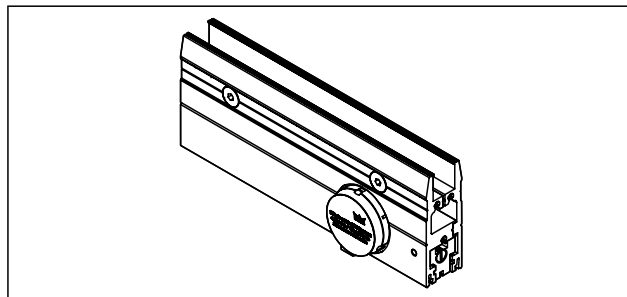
Riegelschloss mit Mikroschalter in Ausführung rechts, für KABA-Rundzylinder
